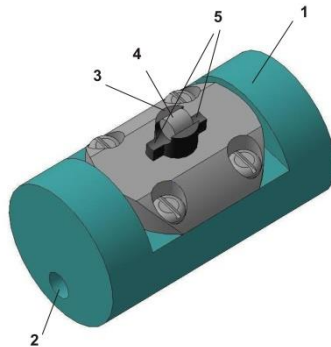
Трехмерный вид гидравлического цилиндра прибора
